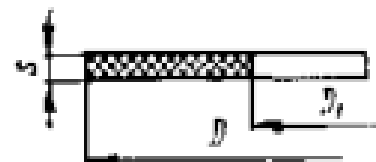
Прокладка из паронита для фланцевых сварных аппаратов.
